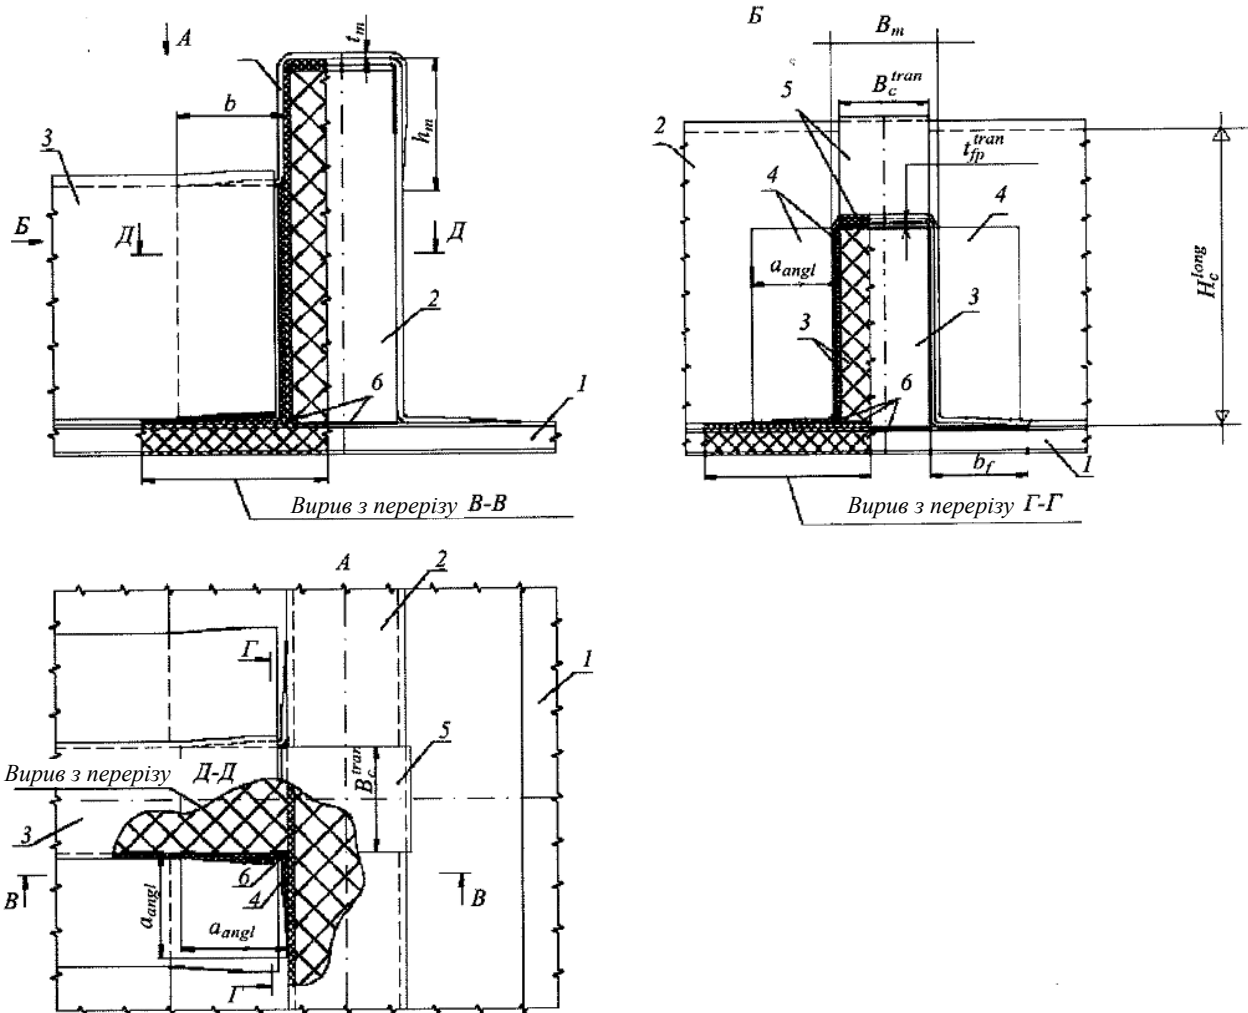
Вузол закінчення і з'єднання поперечної балки з поздовжньою балкою: 1 - обшивка (настил); 2 - поздовжня балка; 3 - поперечна балка; 4 - приформовочні косинці; 5 - накладка; 6 - адгезійна речовина
